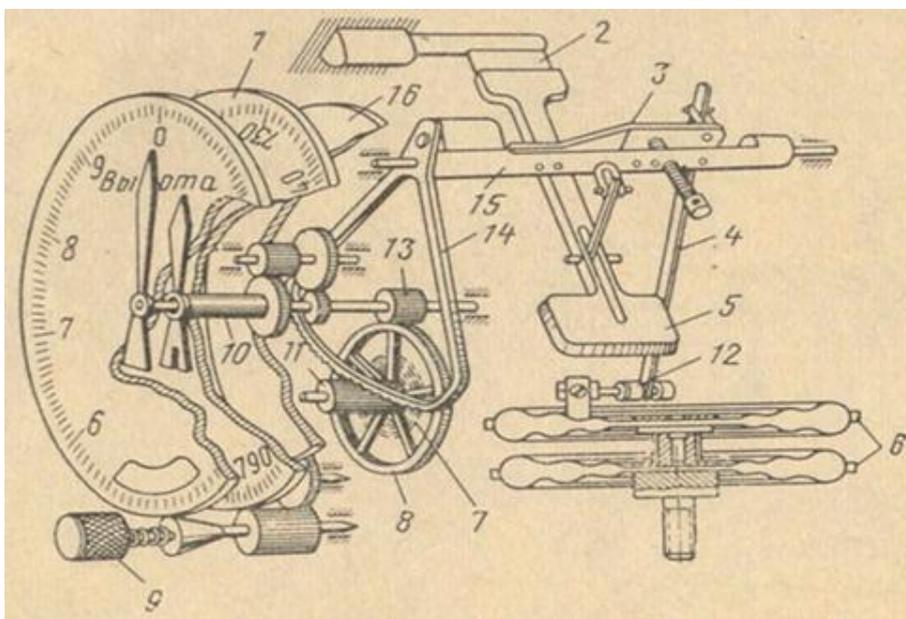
Кинематическая схема двухстрелочного барометрического высотомера
